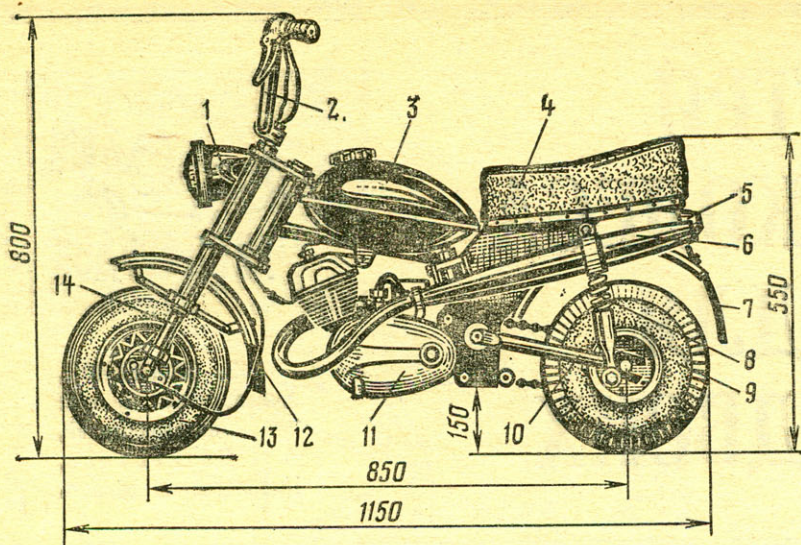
Компонетка микромотоцикла А. Стригалева: 1 — фара, 2 — руль, 3 — топливный бак, 4 — седло, 5 — стоп-сигнал, 6 — глушитель, 7 — задний грязевой щиток, 8 — задний амортизатор, 9 — заднее колесо, 10 — задний маятник подвески, 11 — двигатель Ш-52, 12 — передний грязевой щиток, 13 — переднее колесо, 14 — передний амортизатор.
